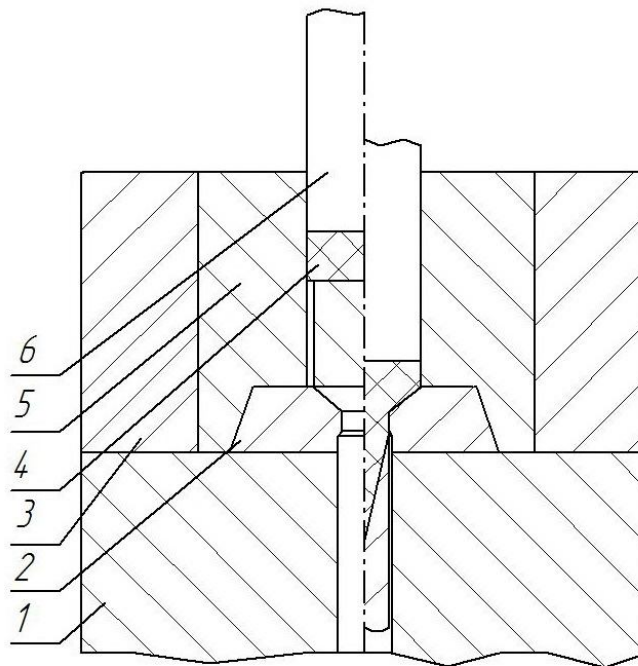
Схема штамп для гарячого видавлювання алюмінієвого прутка: 1 – нижня плита; 2 – вставка; 3 – обойма; 4 – пресовка; 5 – матриця; 6 – пуансон
